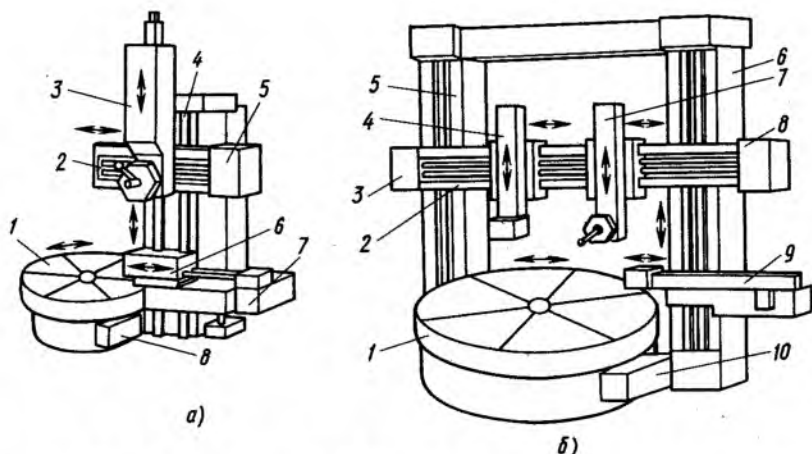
Одностоечный (а) и двухстоечный (б) карусельные станки
